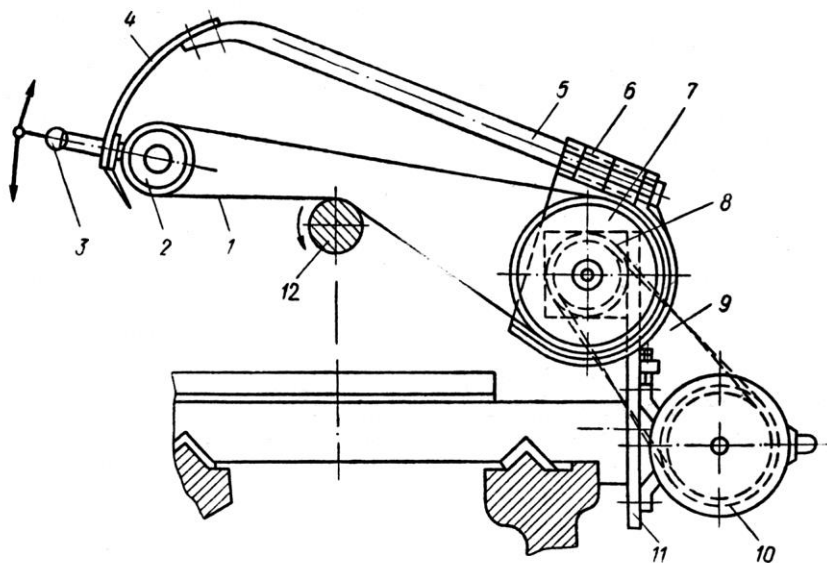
Схема пристрою для полірування деталей безконечною стрічкою: 1 — безконечна стрічка; 2 — ролик; 3 — рукоятка; 4 — пружна пластина; 5 — стержень; 6 — і кронштейн; 7 — шків; 8 — вібратор; 9 — клинопасова передача; 10 — електродвигун; 11 — плита; 12 — деталь
